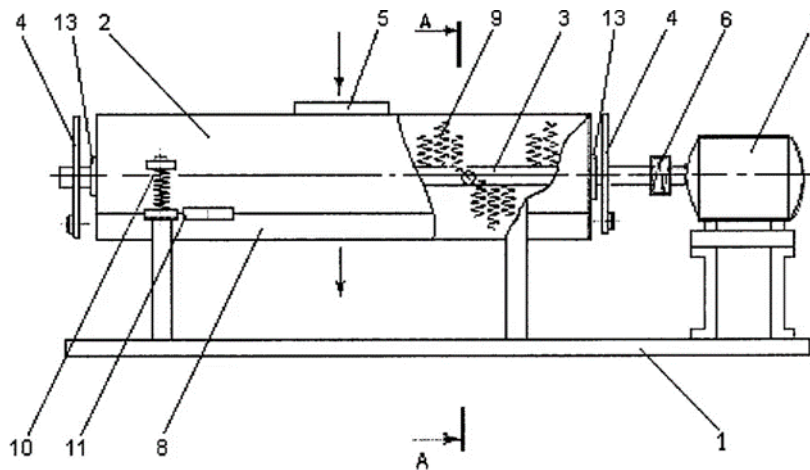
Вибрационный смеситель конструкции Челябинского агроинженерного университета: 1 — рама; 2 — контейнер; 3 — вал; 4 — вибровозбудитель; 5 — загрузочная горловина; 6 — муфта; 7 — электродвигатель; 8 — разгрузочный люк; 9 — перемешивающие пружины; 10 — пружины; 11 — шарнир; 12 — защелка; 13 — торцевые стенки
